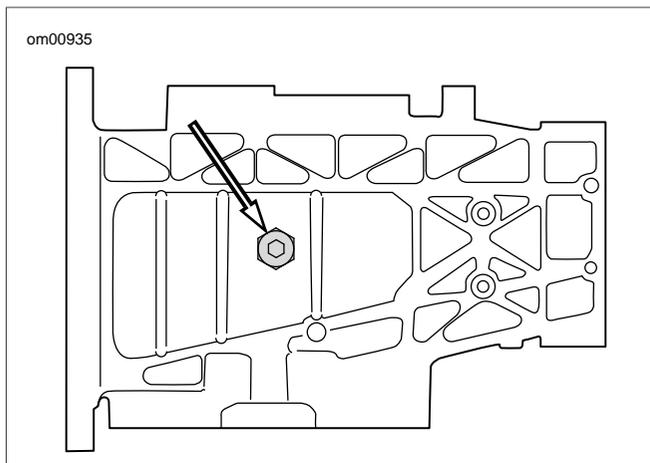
Getriebeölablassschraube (Ansicht von unten)
